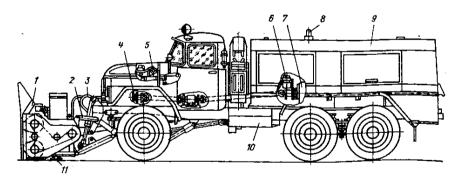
Шнекороторный снегоочиститель Амкодор-9531 (ДЗ-226): 1 – рабочий орган; 2 – подвеска рабочего органа; 3 – гидросистема; 4 – привод рабочего органа; 5 – система обогрева кабины; 6 – система пневмотормозов; 7 – силовая установка; 8 – светосигнальный фонарь; 9 – капот; 10 – аккумуляторы; 11 – опорное устройство
